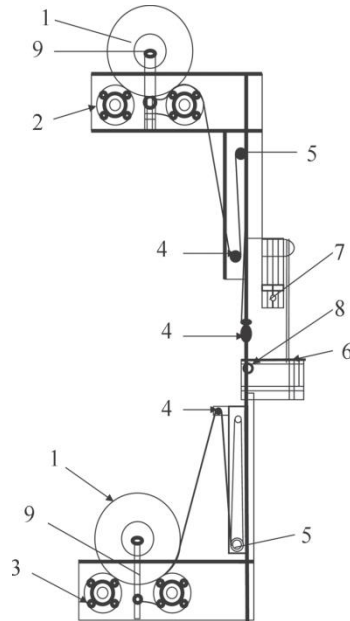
Пристрій для розмотування рулонів і зварювання плівки:
